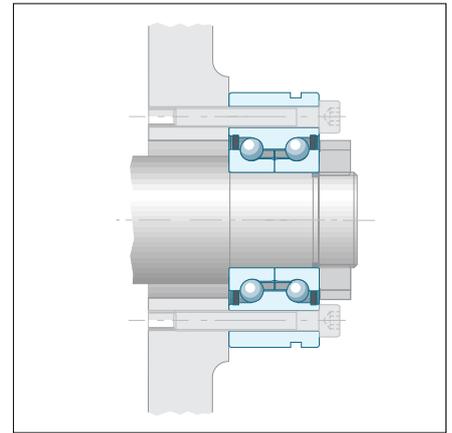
Roulement à billes à contact oblique de la série ZKLF fixé sur une surface plane fraisée
